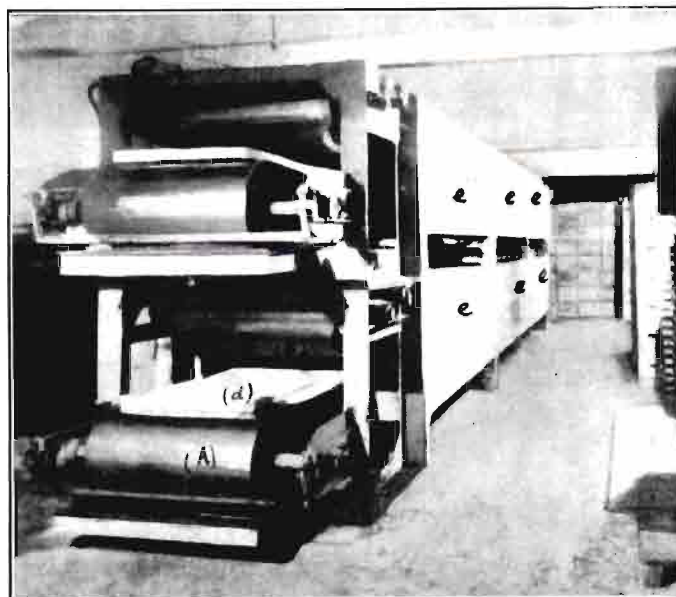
ª—Máquina de congelar, vista desde otra posición.
